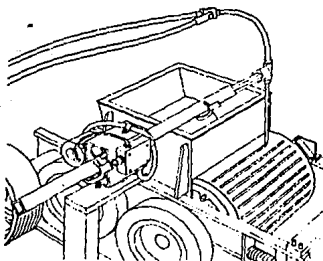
MAQUINA DE SOLDADURA AUTOMATICA
